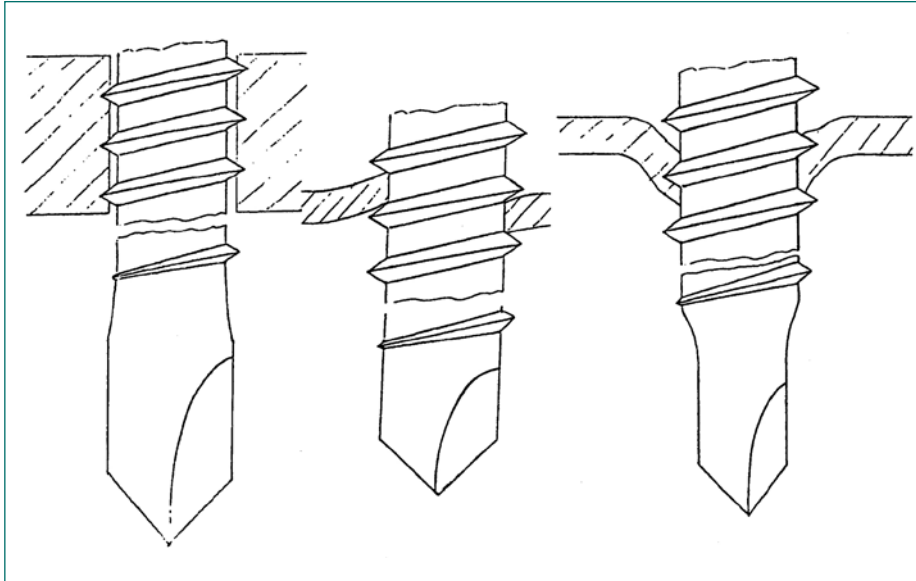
Vergleich der Verkrallung von Gewindeschneid-schraube, Bohr-schraube und Quetschbohr-schraube (von links nach rechts) [Quelle: EJOT Baubefestigungen].
